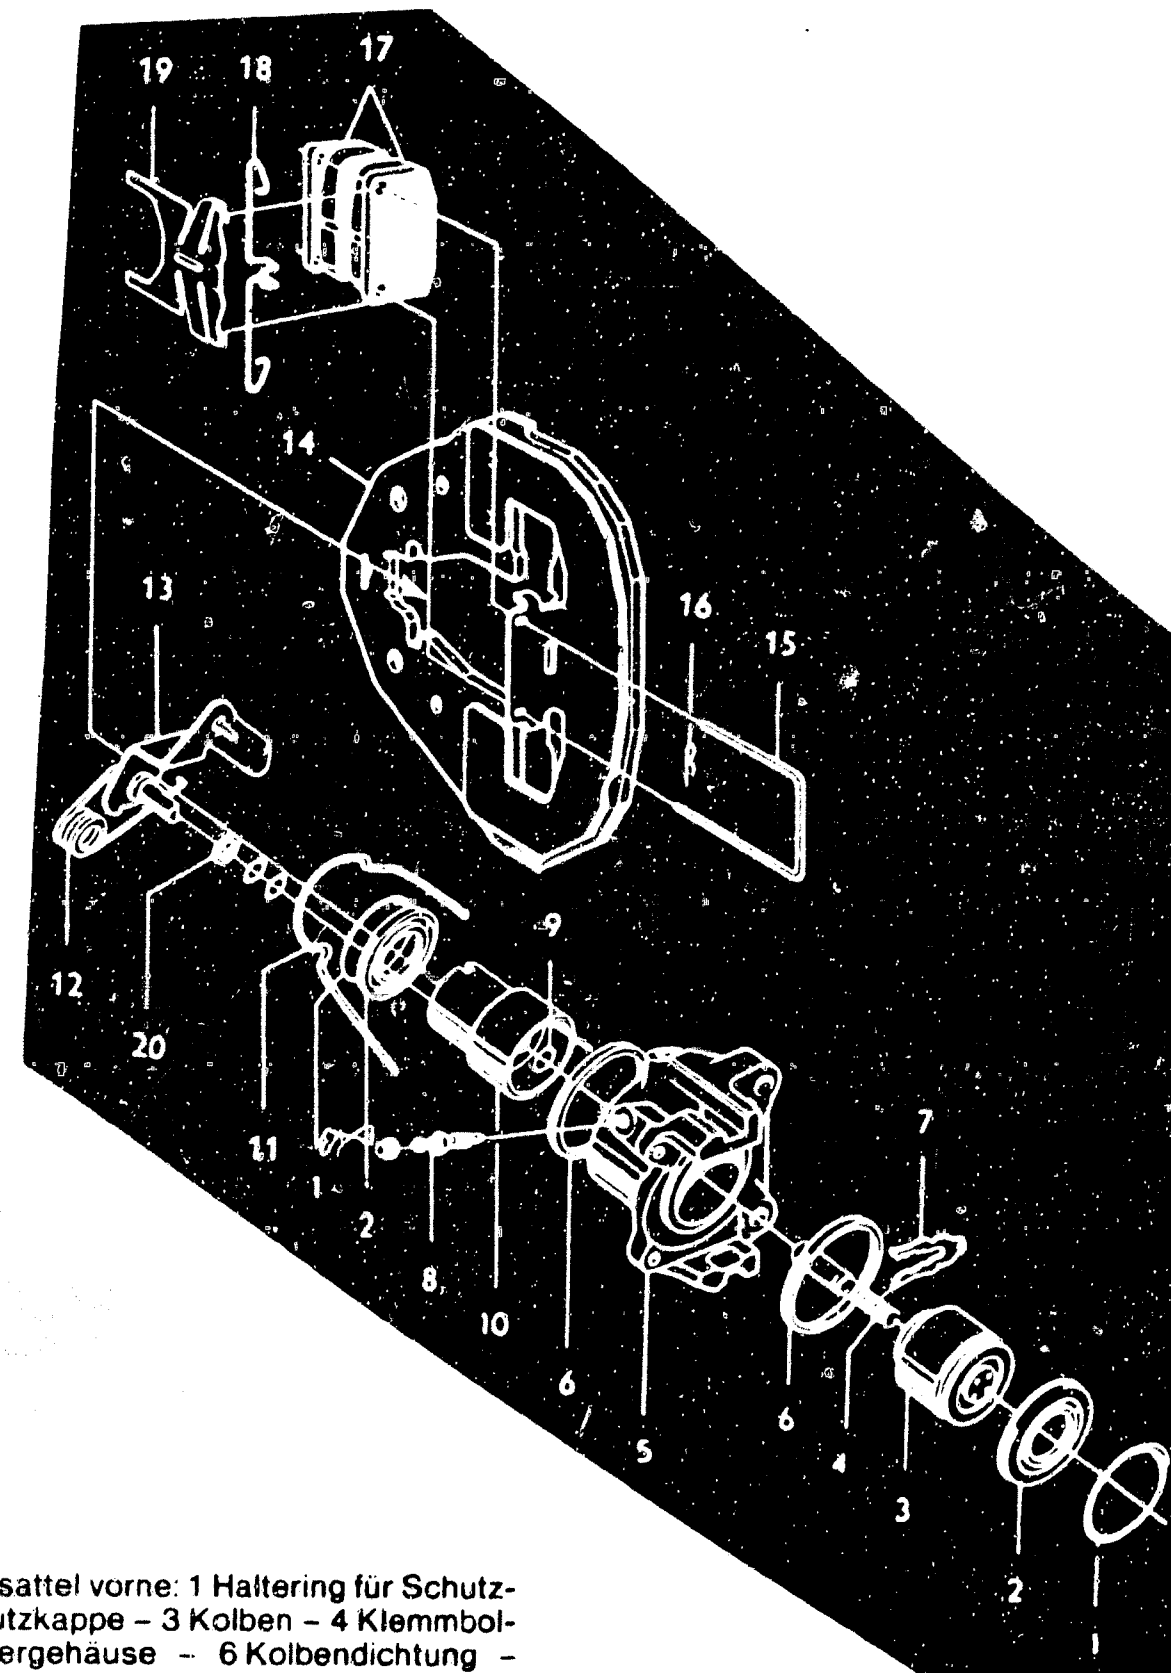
Bremssattel vorne: 1 Haltering für Schutzkappe – 2 Schutzkappe – 3 Kolben – 4 Klemmbolzen – 5 Zylindergehäuse – 6 Kolbendichtung – 7 Sicherung – 8 Entlüftungsschraube – 9 O-Ring – 10 Jochkolben – 11 Jochfeder – 12 Handbremshebel-Feder – 13 Handbremshebel – 14 Joch – 15 Bremsklotzhaltebügel – 16 Sicherungsöse – 17 Bremsbeläge – 18 Feder – 19 Jochfeder – 20 Halter (2 O-Ringe).
